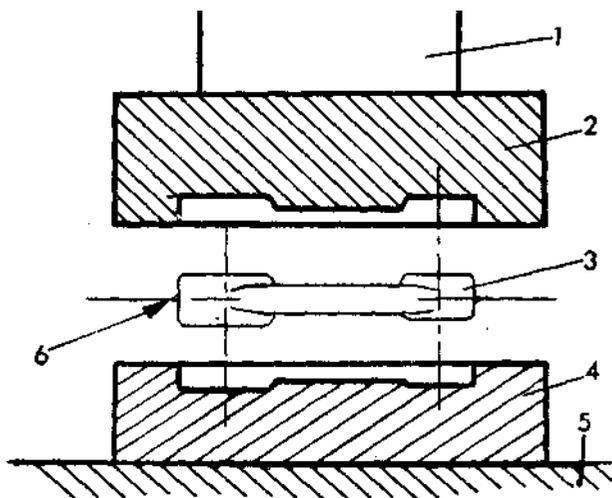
Forma de estampar una pieza.—1. Brazo de la prensa.—2. Parte superior de la matriz.—3. Pieza estampada.—4. Parte inferior de la matriz.—5. Mesa de la prensa.—6.Rebabas.
